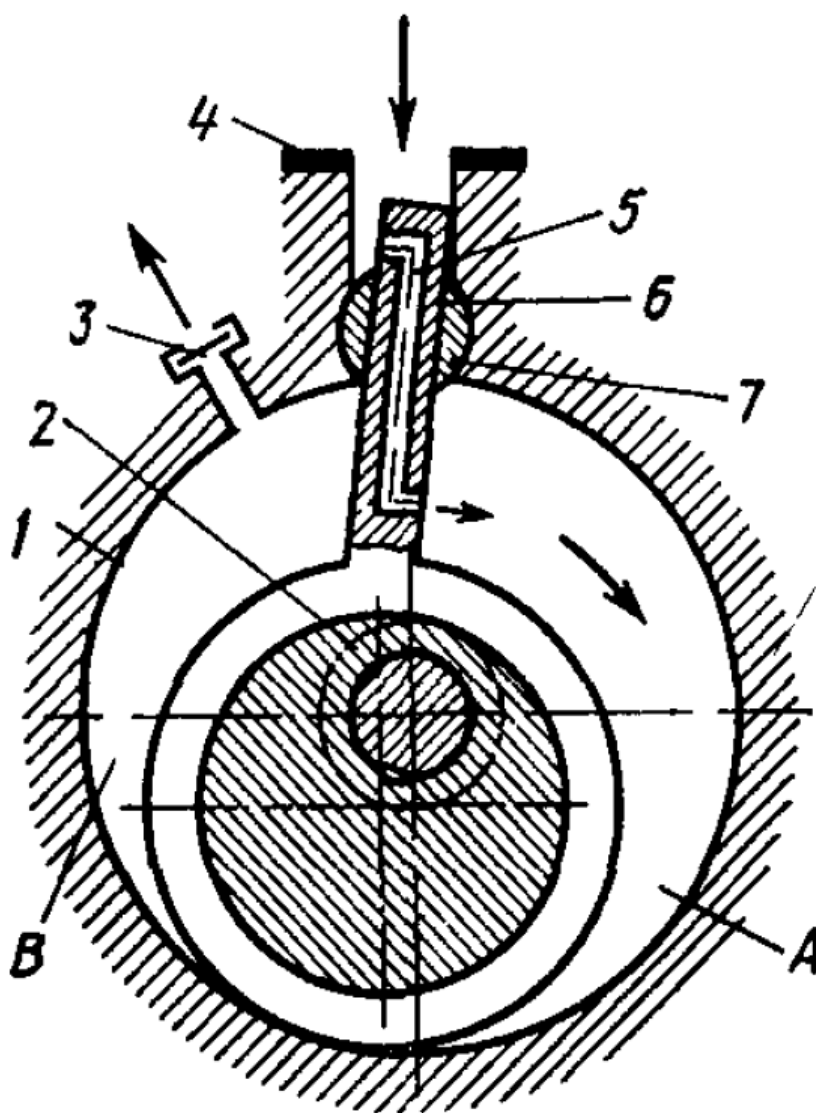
Схемы устройства плунжерного (золотникового) насоса. 1 – цилиндрический корпус; 2 – эксцентрический ротор; 3 – выхлопной патрубок с обратным клапаном; 4 – входной патрубок; 5 – канал золотника; 6 – плунжер; 7 – шарнир [7, с. 166]
